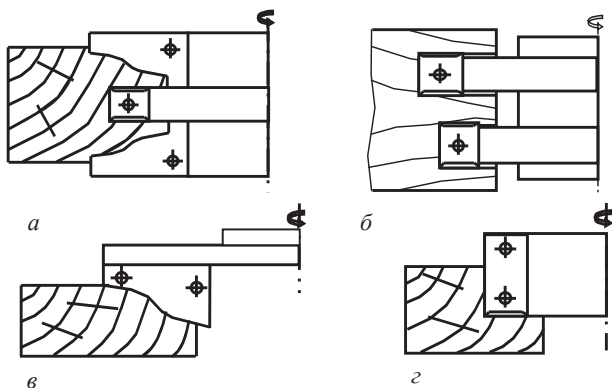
Обработка профилей деталей: а – бруска двери; б – бруска дверной коробки; в – мебельной филенки; г – выборка четверти
